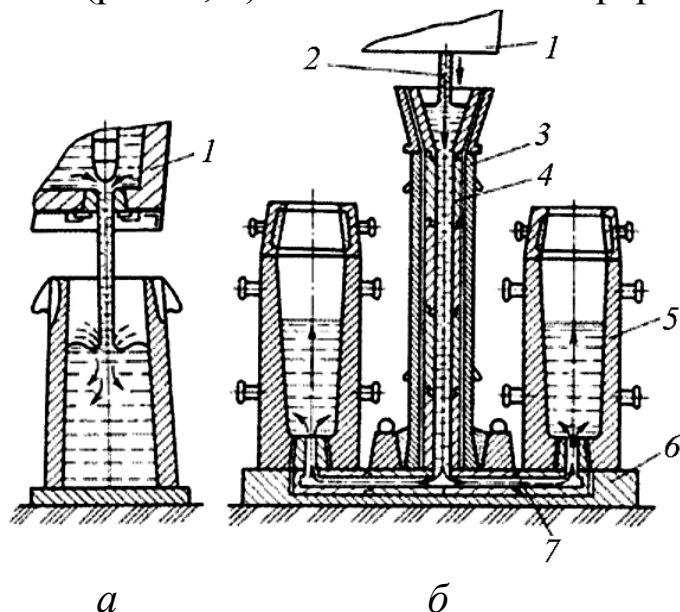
Разливка стали в изложницы: а – сверху; б – снизу (сифоном)
